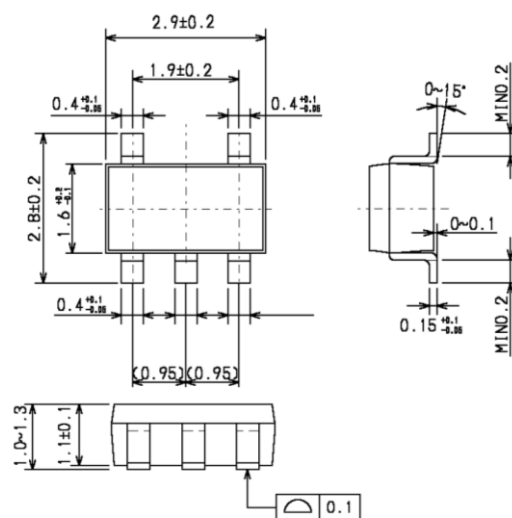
Цоколевка и размеры стабилизатора напряжения
